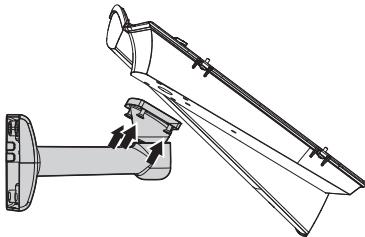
Fixation sur support avec passage intérieur des câbles.
